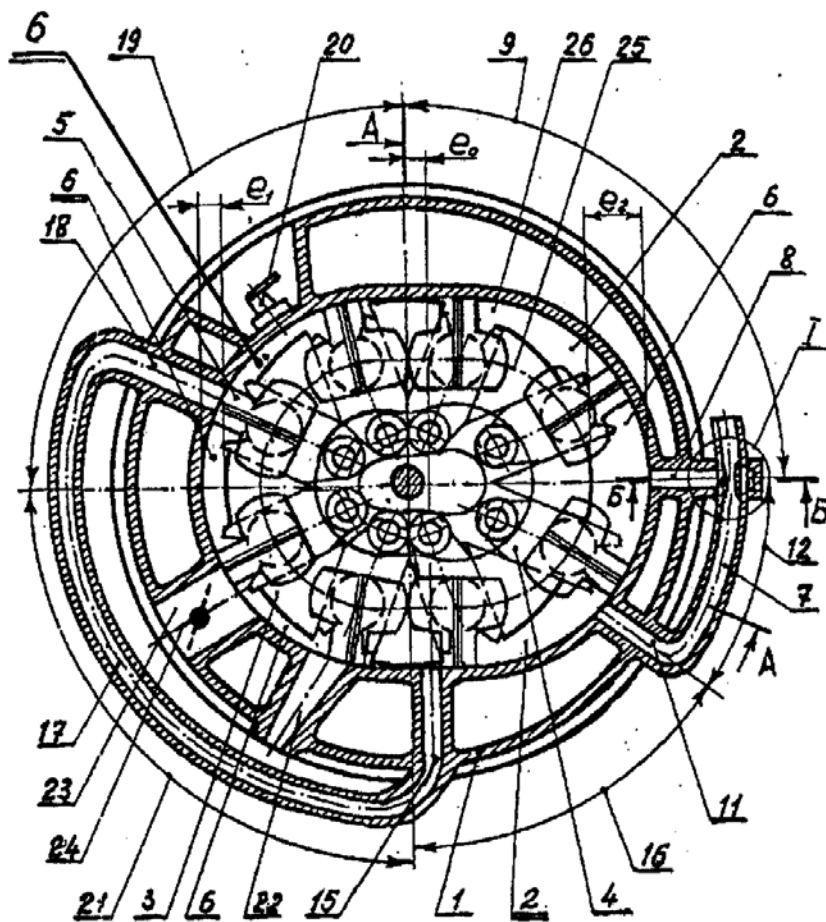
Поперечный разрез двигателя с тороидально-цилиндрической рабочей поверхностью
